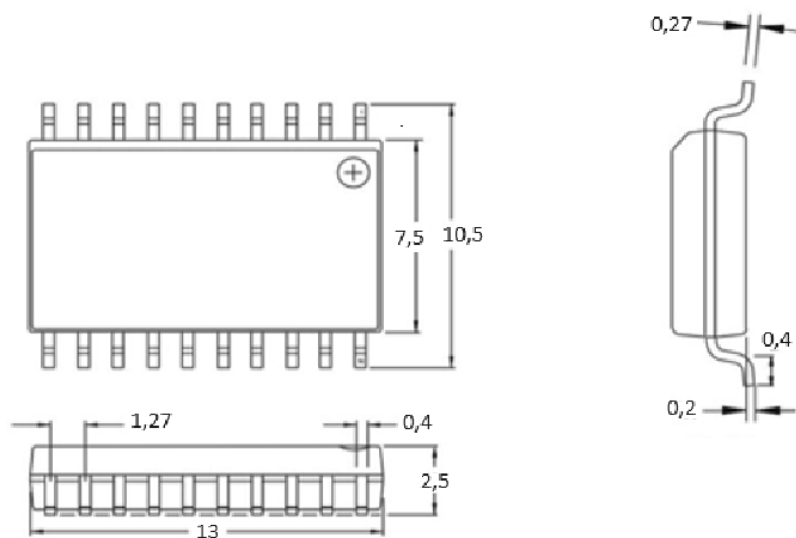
Зовнішній вигляд та габаритні розміри мікроконтролера ATtiny2313 в корпусі SOIC-20
